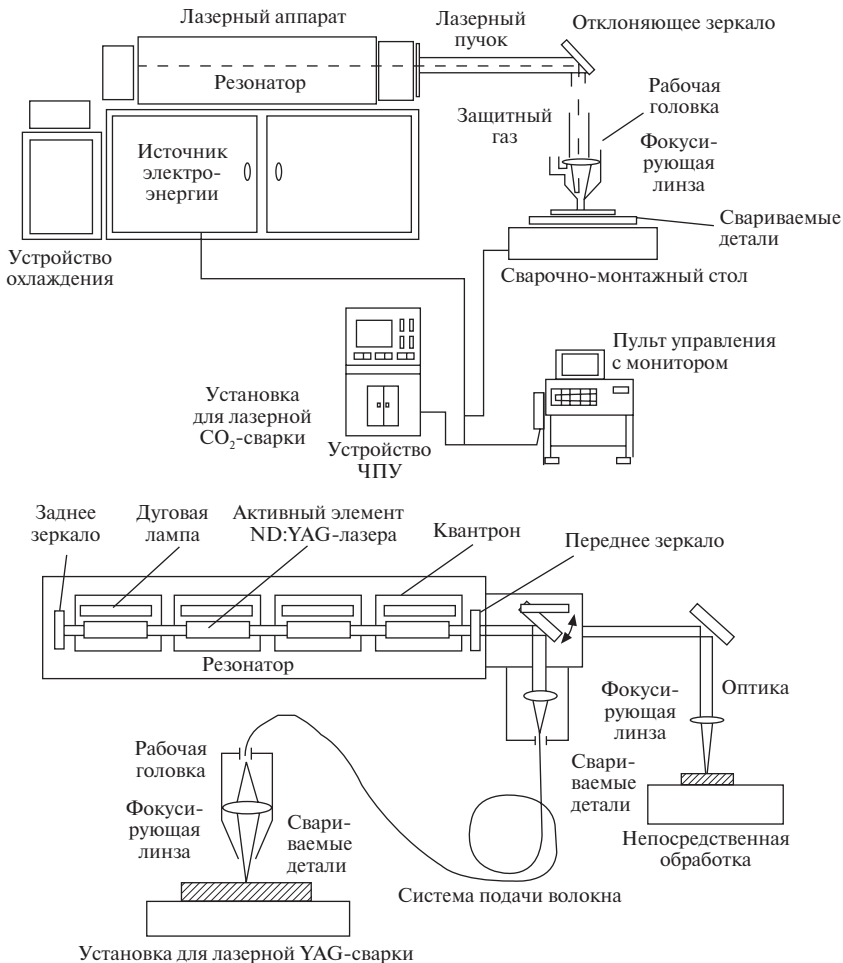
Схема систем YAG- и CO₂-лазерной сварки
